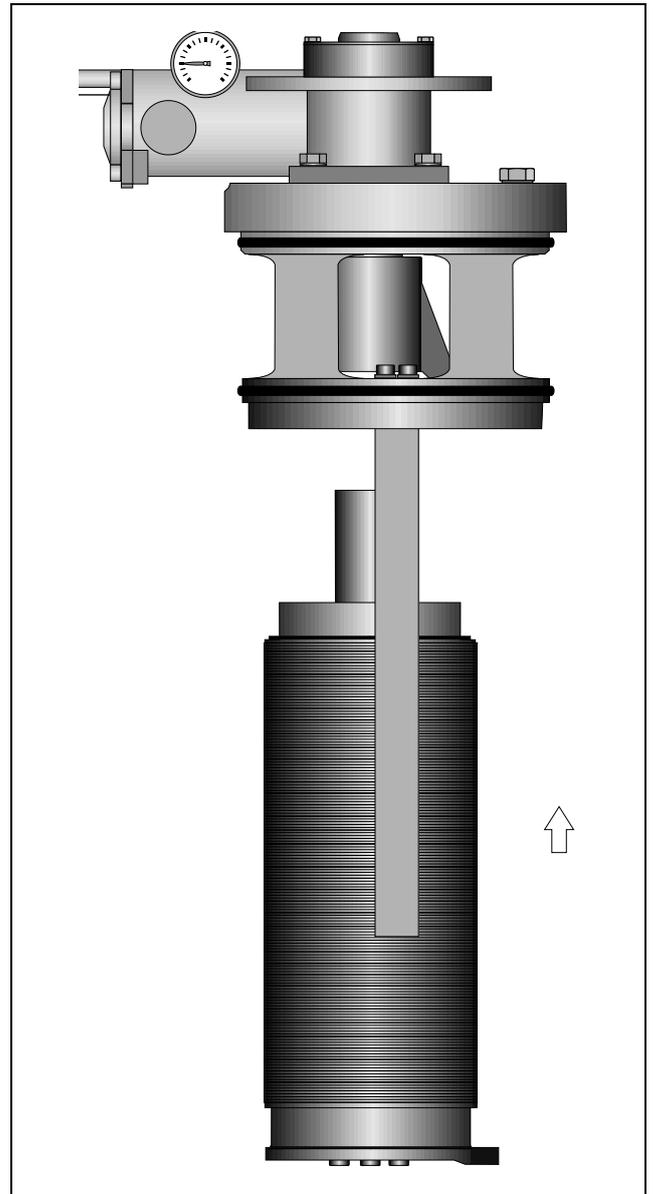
Vormontierte Baugruppe in Antriebswelle einbauen
